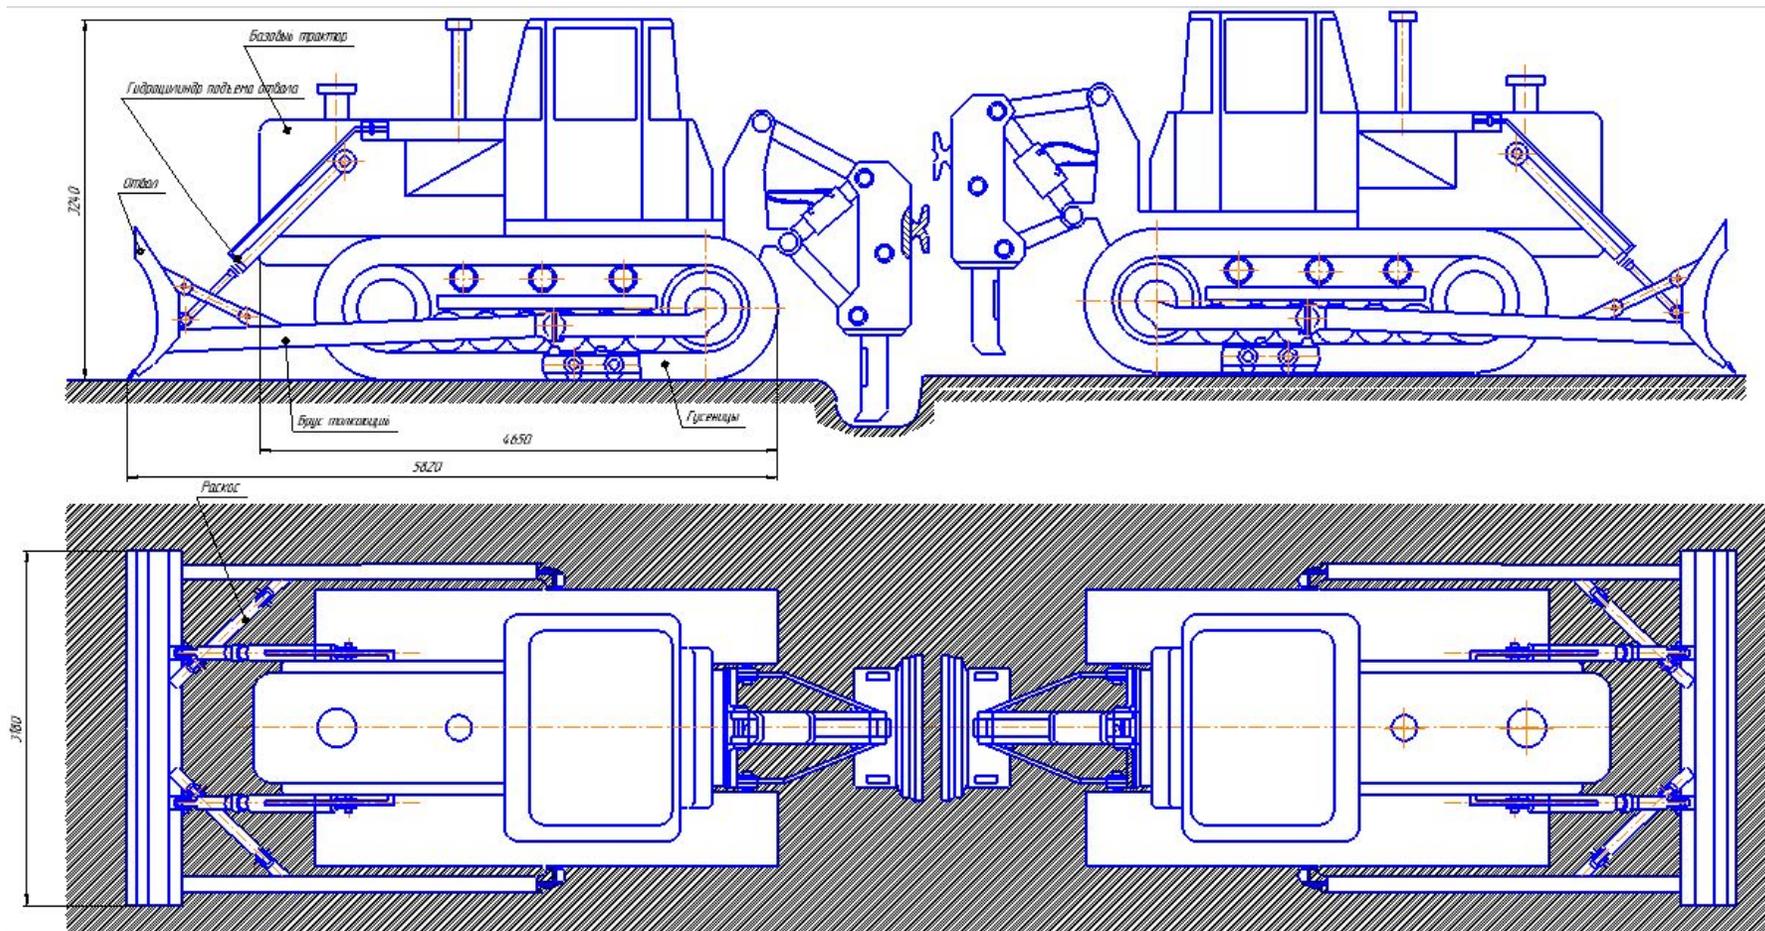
Бульдозер-рыхлитель с сварным креплением
